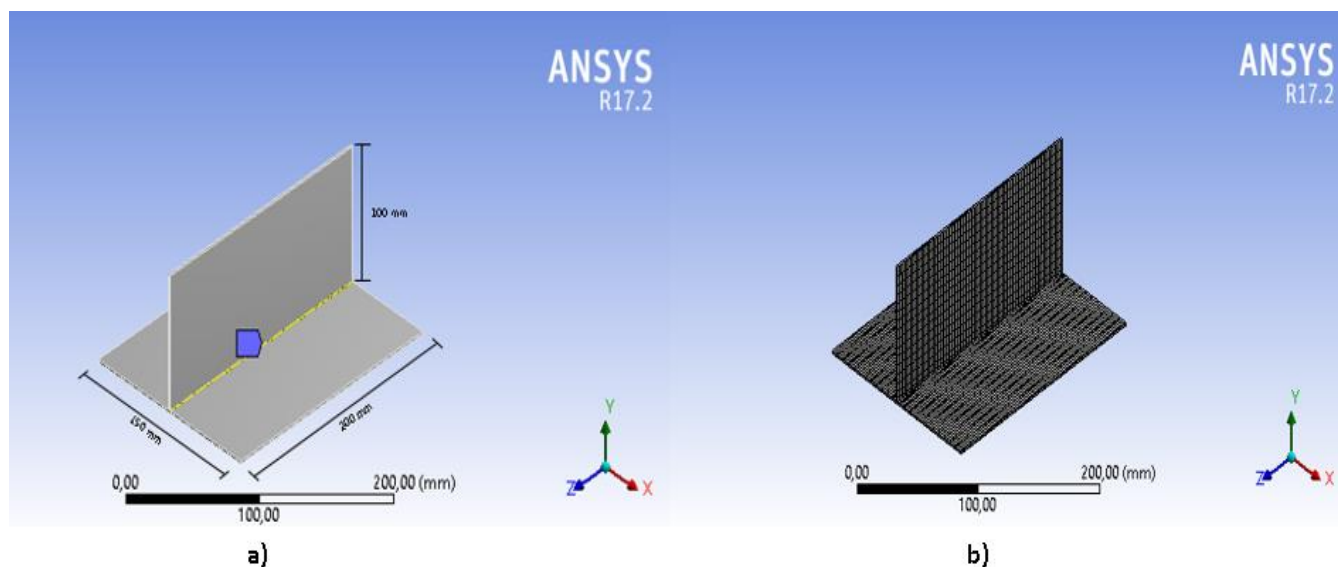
a) Geometria e dimensão da peça soldada. b) Malha da peça.
